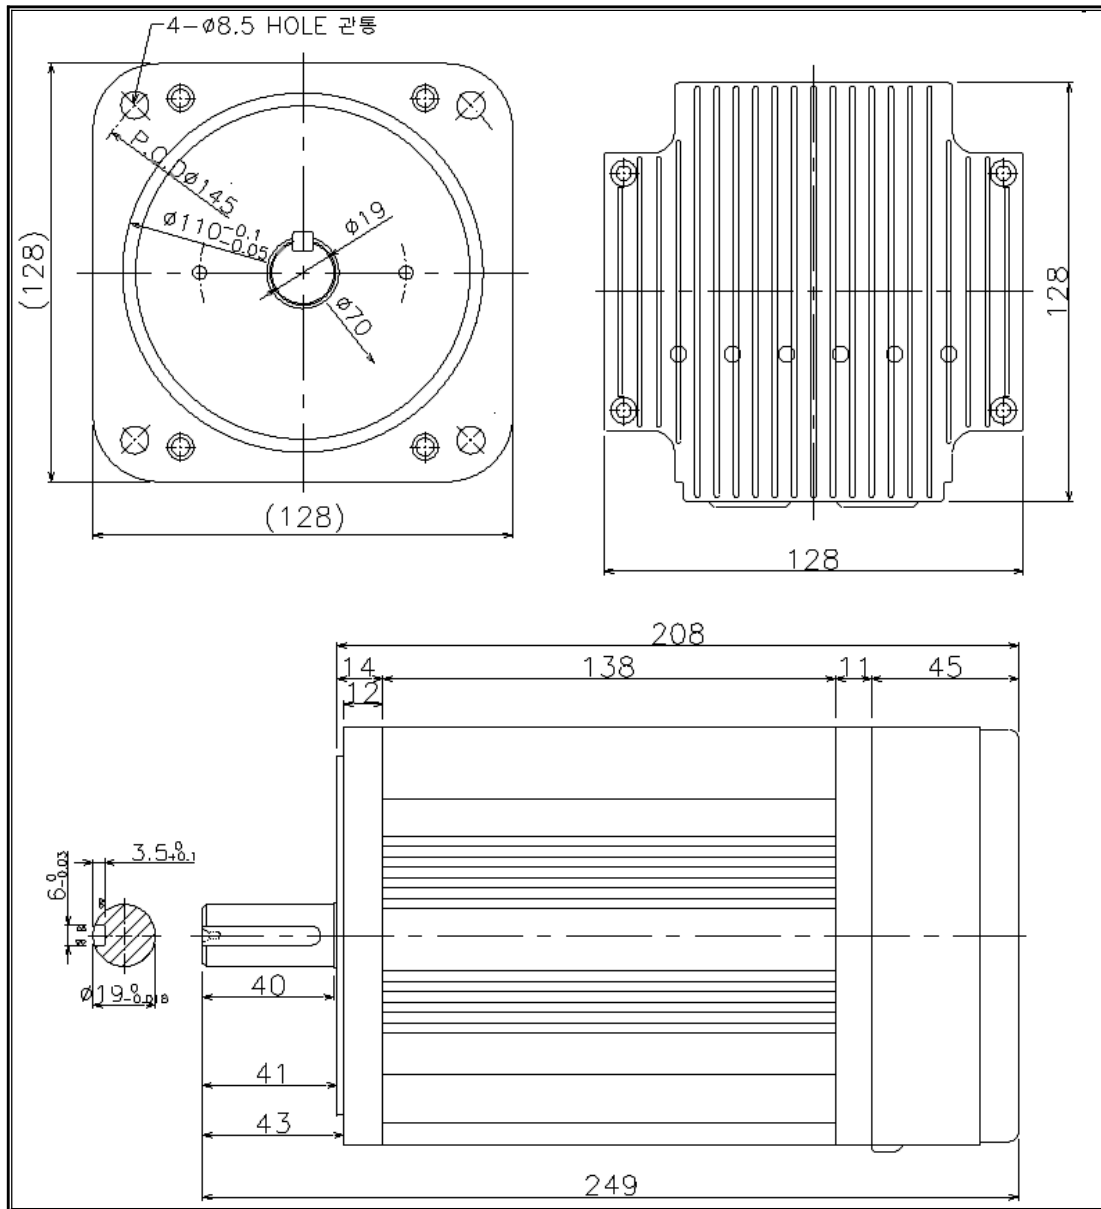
BLDC MOTOR 외형도 (1.5KW TM13-A1523,A1533,A2053시리즈)
